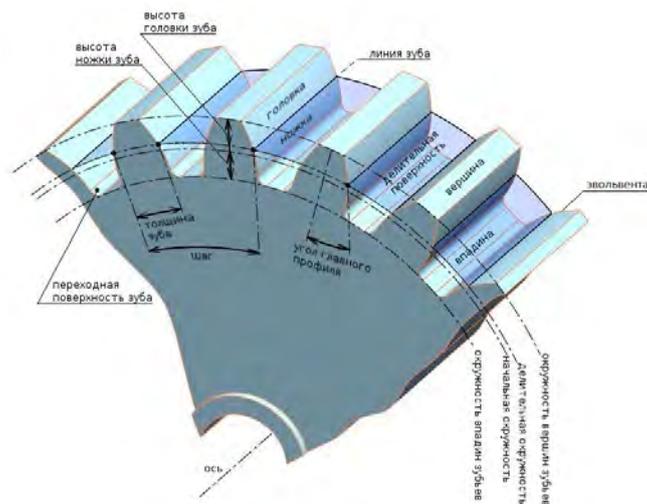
Основные параметры цилиндрического зубчатого колеса
